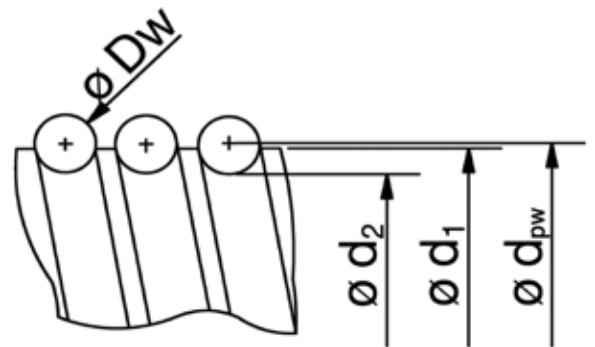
Abmessungen gewirbelte Gewindespindeln
